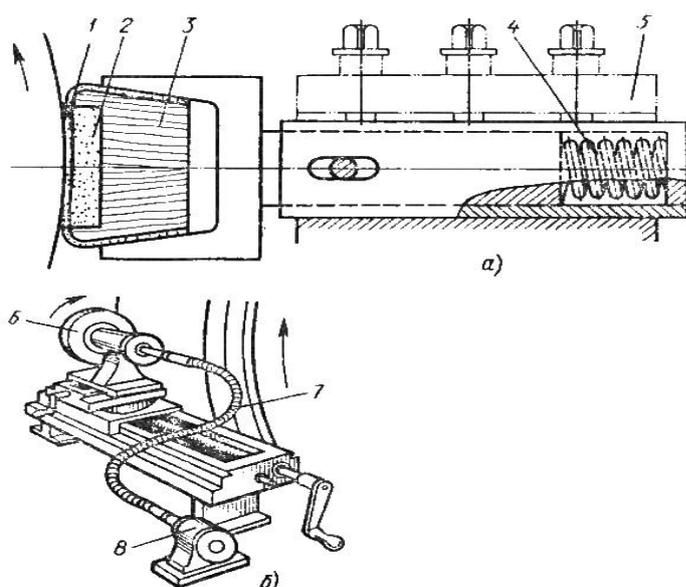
Приспособление для полировки (а) и шлифовки (б) коллекторов: 1 — абразивная бумага; 2 — упругая прокладка; 3 — колодка; 4 — пружина; 5 — супорт; 6 — абразивный круг; 7 — гибкий вал; 8 — электродвигатель.
